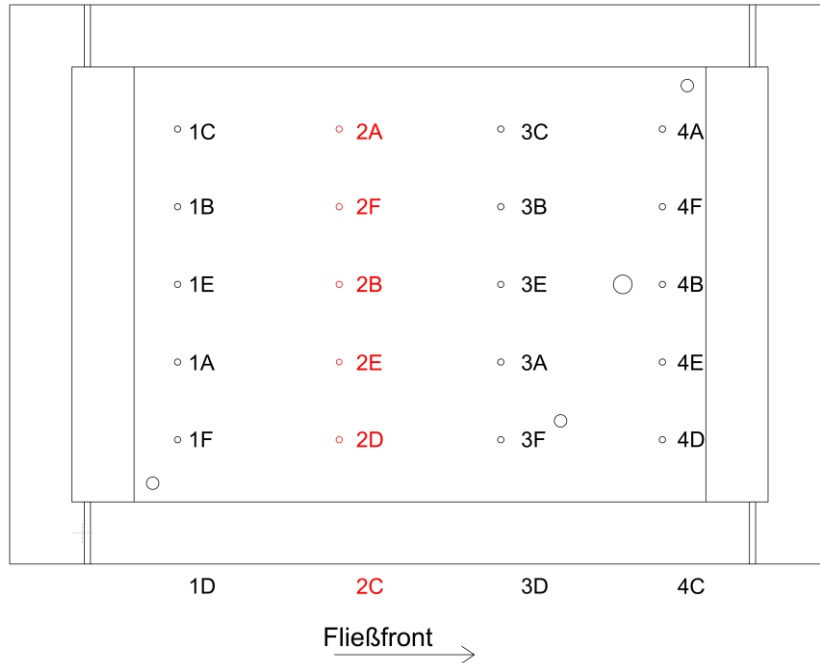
Positionen der Ultraschallsensoren im open mold Formwerkzeug [INVENT GmbH]
